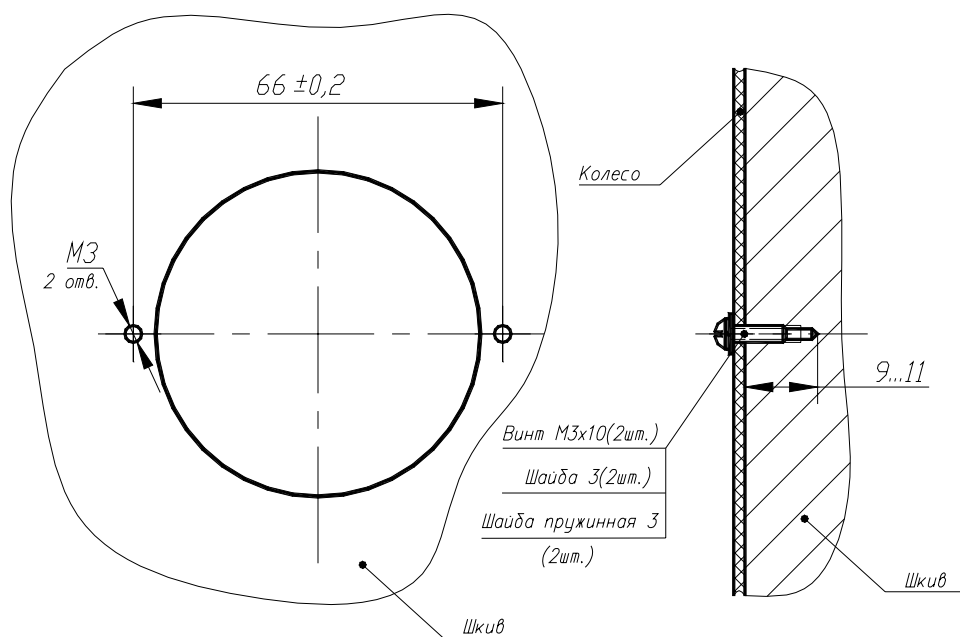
Отметка центра отверстий крепления колеса на шкиве и крепление колеса к шкиву.
